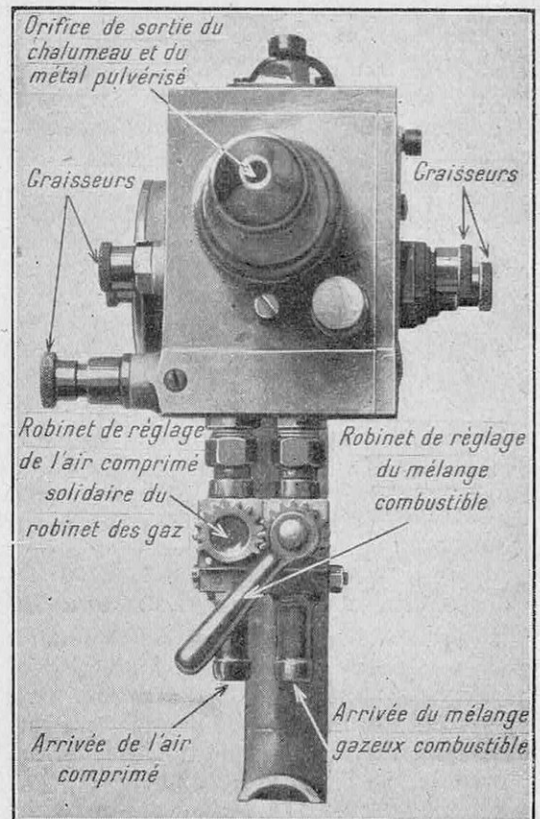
VUE DE FACE DU PISTOLET « SCHOOP »
